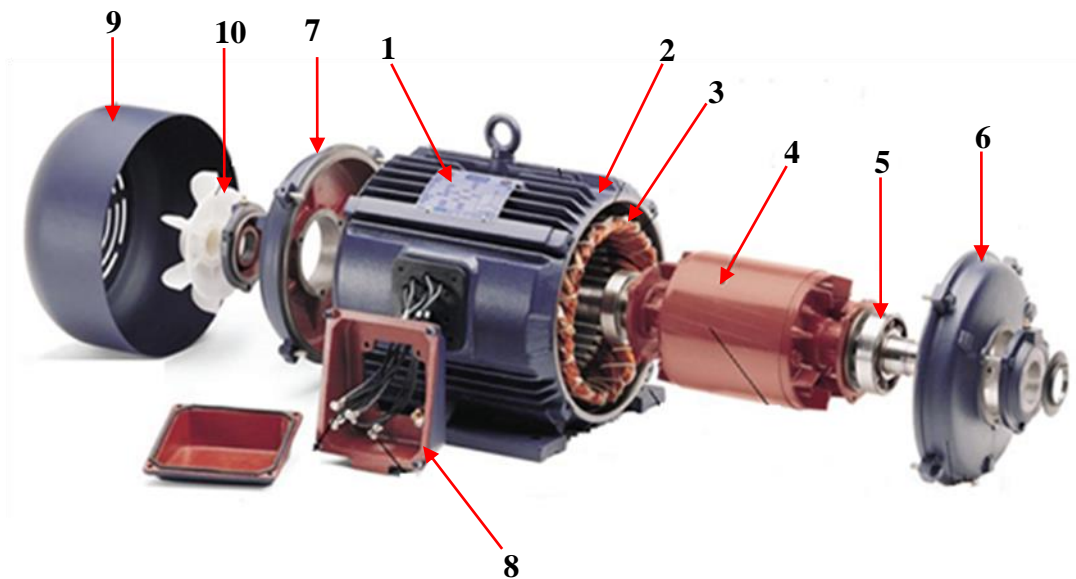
Machine asynchrone à cage d'écurieil : 1-Plaque signalétique 2- Stator, 3-Bobinée statorique, 4-Rotor, 5- Roulement, 6- Flasque palier cote bout d'arbre, 7- Flasque palier cote ventilateur, 8- Plaque a borne, 9- Capot de ventilateur, 10- Ventilateur
